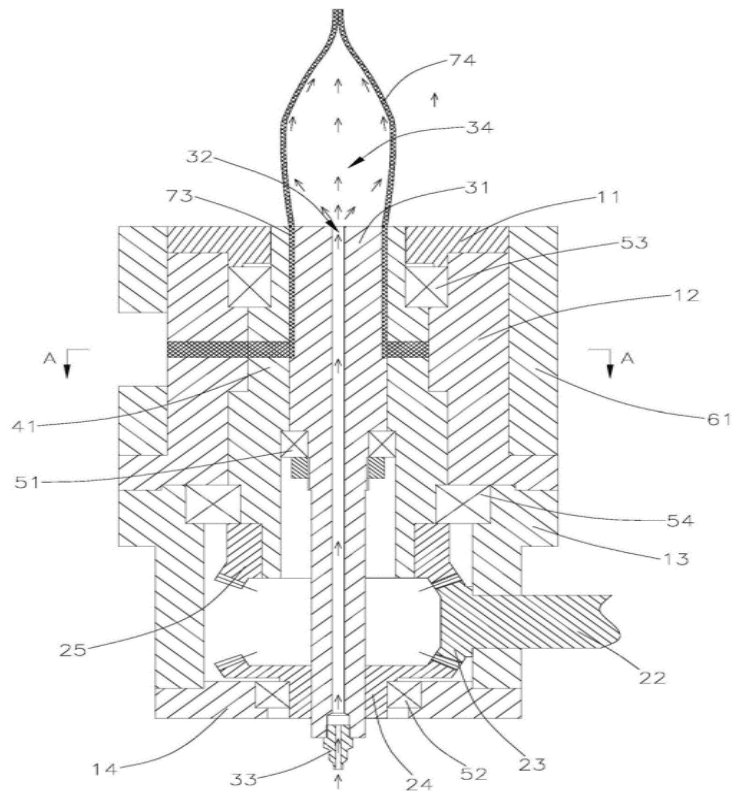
Конструкція багатошарової головки видувного формування плівки з різноспрямованим обертанням:
